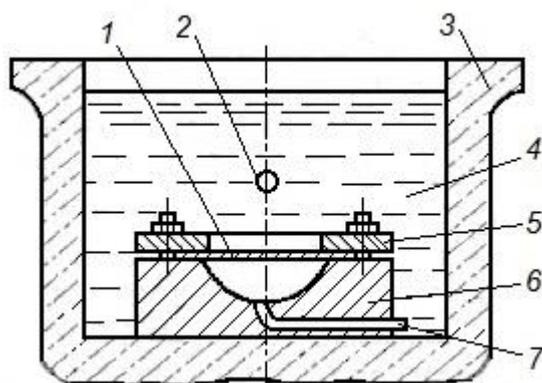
Схема штамповки взрывом деталей из плоской заготовки:
